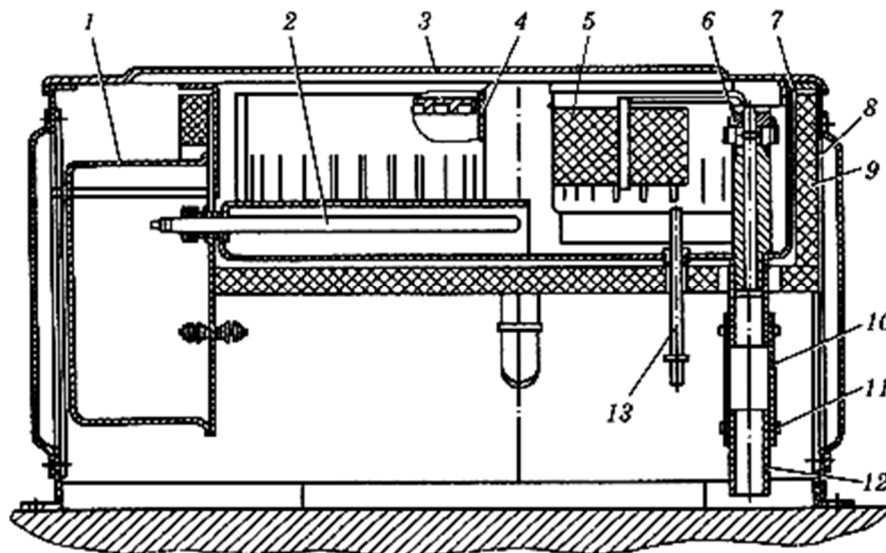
Конструктивна схема групової напувалки АГК-4Б:
